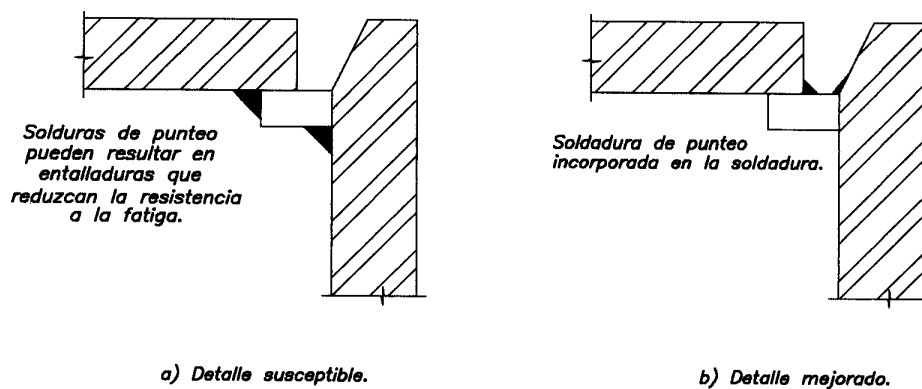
Efectos de la soldadura de punteo en la plancha de respaldo.
